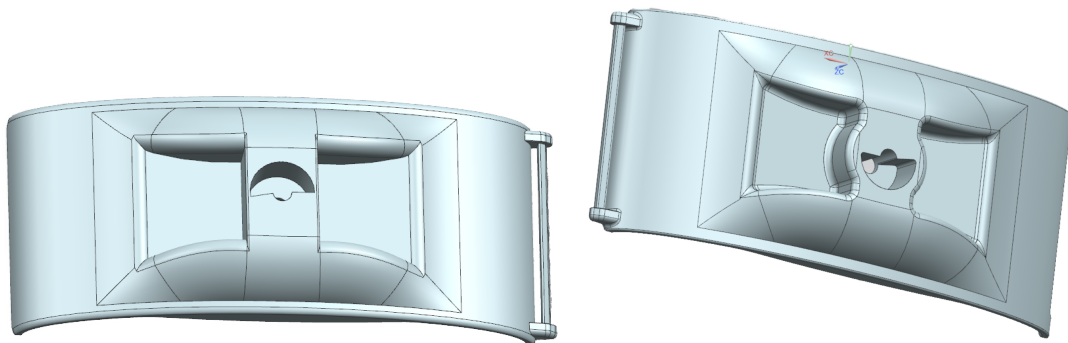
Diseño definitivo soporte mano vistas; Fuente propia
